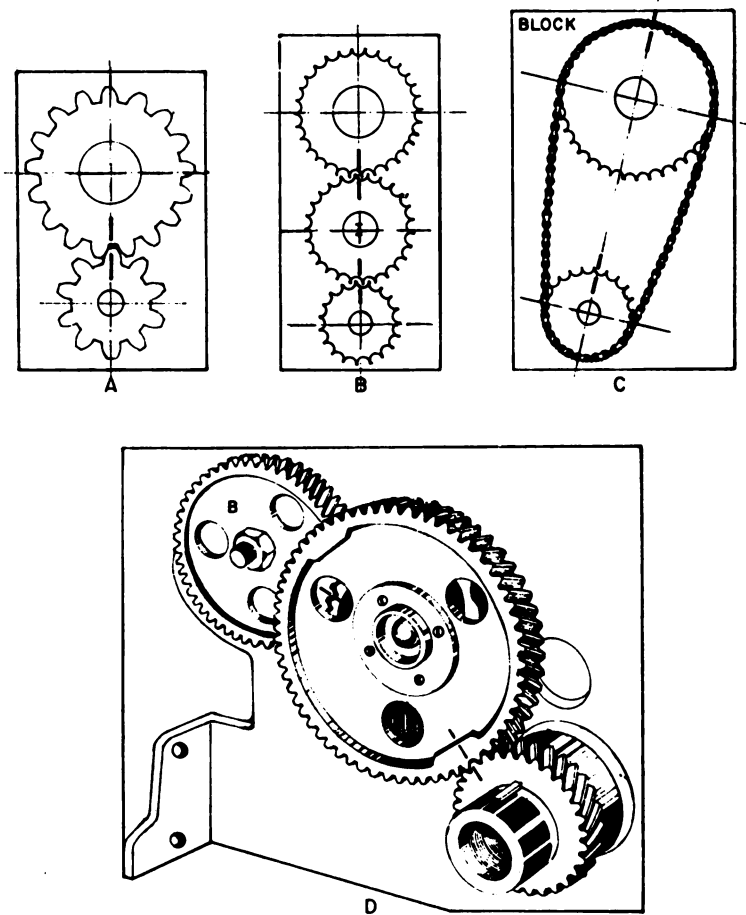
A) Sincronización de dos engranajes de distribución; B) Sincronización con engranaje intermediario; C) Sincronización por cadena; D) Sincronización de engranajes de un motor Diesel.
